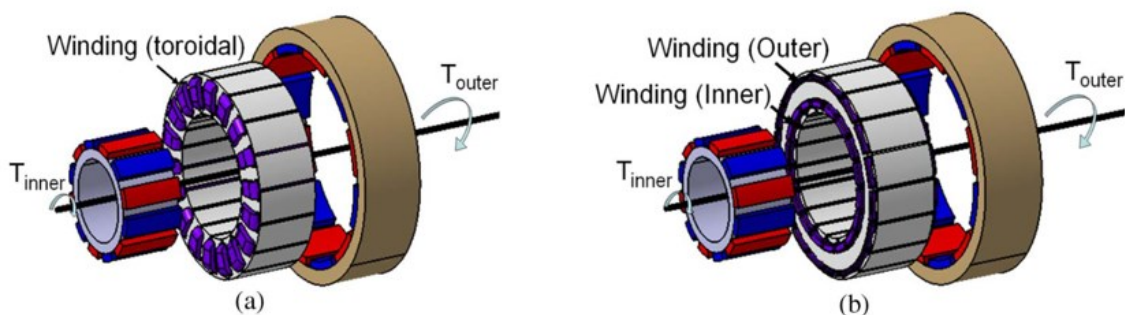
Vue éclatée du bobinage (a) toroïdal et (b) radial de la machine à double rotor comprenant 12 pôles au rotor et 18 encoches au stator [3]
